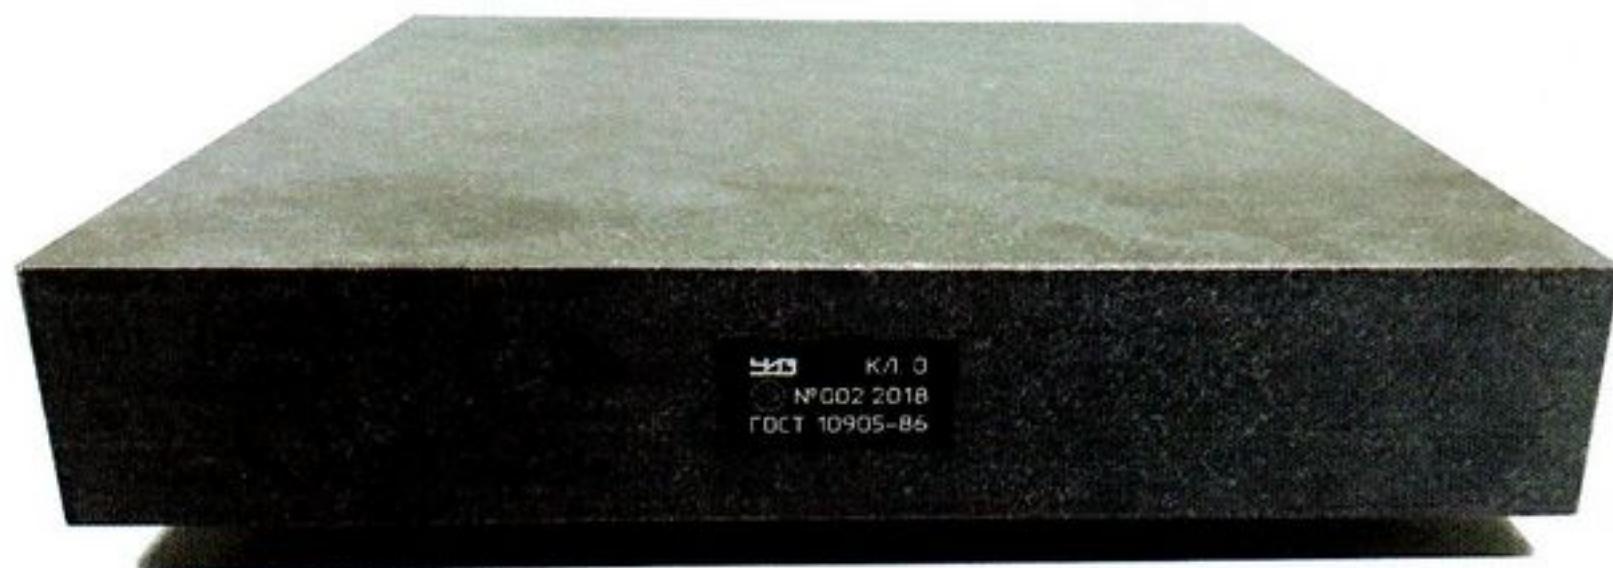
Общий вид плиты поверочной и разметочной исполнения 3
